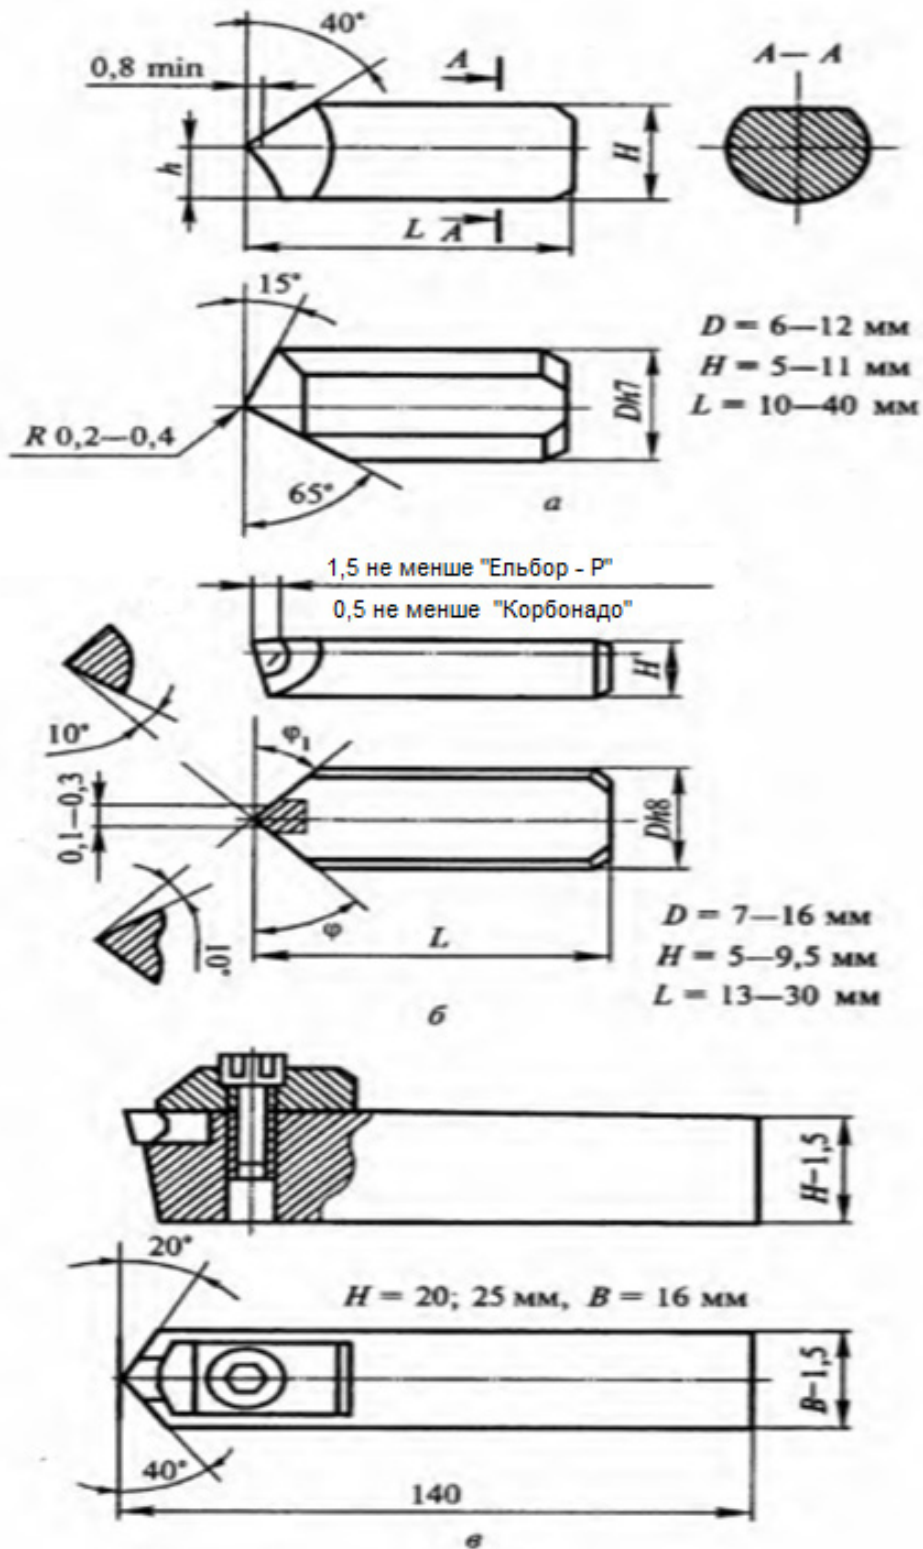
Циліндричні вставки і збірний різець з різальними елементами з НТМ: *a* – з напайним алмазом; *б* – з ельбором-Р, закріпленним методом порошкової металургії; *в* – прохідний різець з механічним кріпленням вставки
